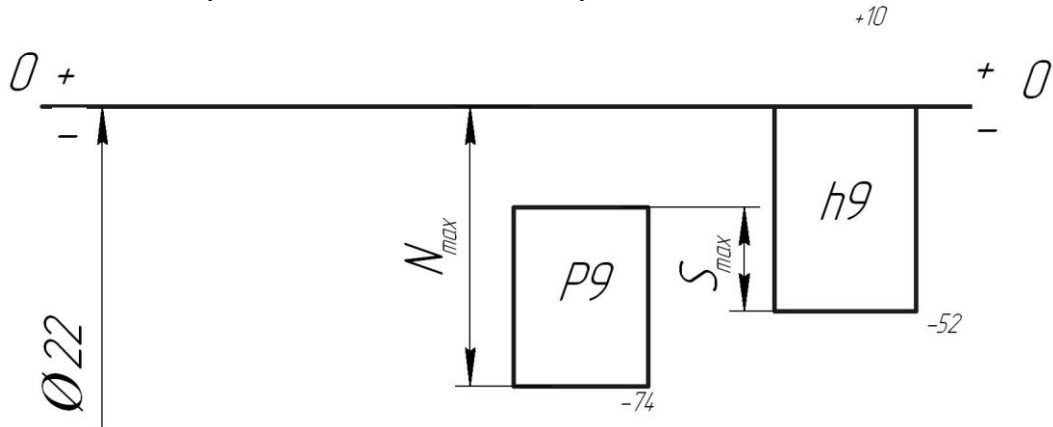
Схема полей допусков соединения шпонка - паз втулки
